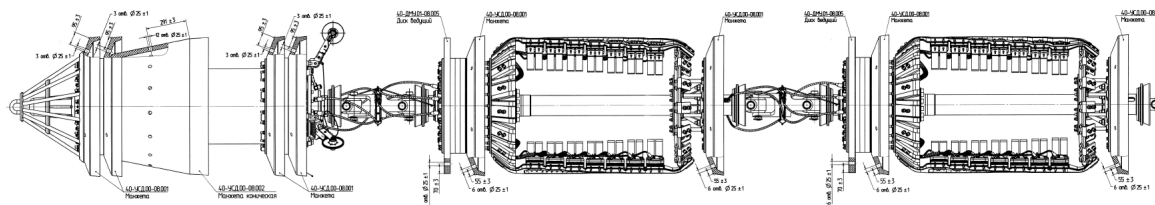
Эскиз общего вида дефектоскопа внутритрубного ультразвукового 40-ДВУ.00-00.000 в типоразмере 1020 мм (40")
